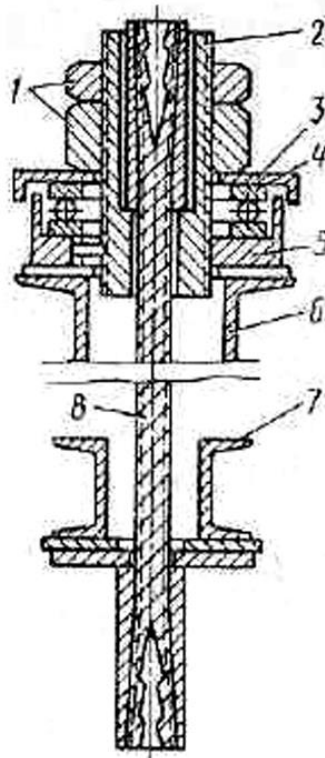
Вузол підвіски: 1 – регулювальна гайка; 2 – натяжна муфта; 3 – захисна шайба; 4 – шарикопідшипниковий упор; 5 – ліжко підшипника; 6 – стійка; 7 – опорна рама; 8 – трос
